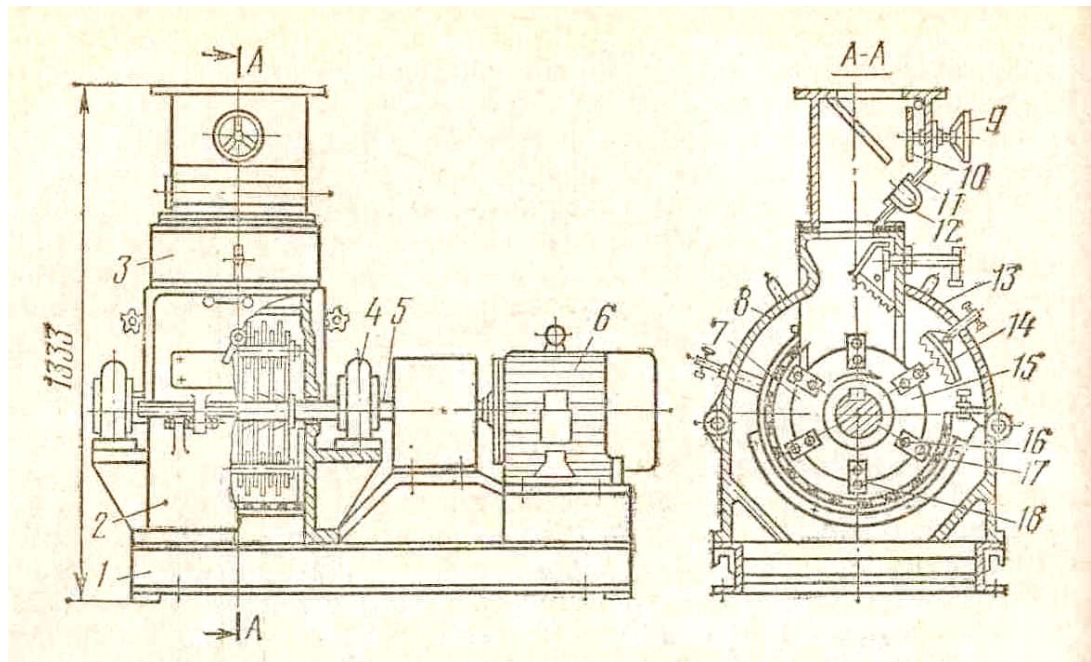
Молоткова дробарка ДМ: 1 – рама; 2 – основа корпусу; 3 – середня частина; 4 – корпус підшипника; 5 – вал; 6 – електродвигун; 7 – ротор; 8 – ліва кришка; 9 – маховик; 10 – засувка; 11 – живник; 12 – магнітний захист; 13 – права кришка; 14 – дека; 15 – диск; 16 – вісь; 17 – решето; 18 – молоток; 19 – перегородка» [9].
